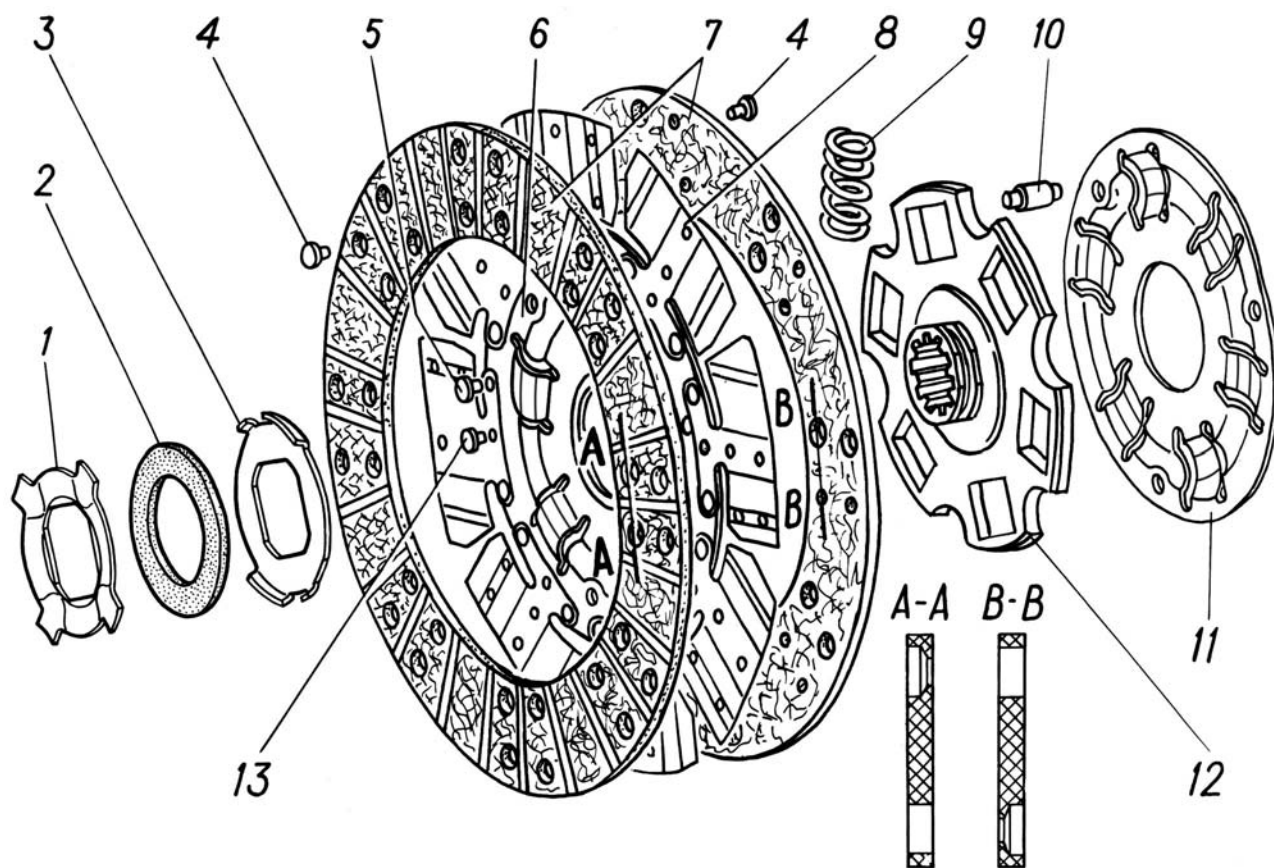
Детали ведомого диска: 1 - нажимная пружина; 2 - теплоизолирующая шайба; 3 - фрикционная шайба; 4 и 5 - заклепки; 6 и 11 - диски; 7 - фрикционные накладки; 8 - пластинчатая пружина; 9 - пружина демпфера; 10 - палец; 12 - ступица; 13 - балансировочный грузик
